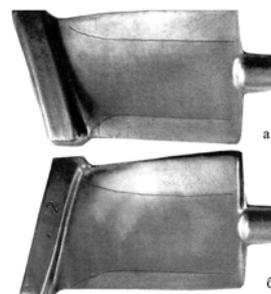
Макроструктура поверхности пера рабочих лопаток компрессора из сплава BT8
